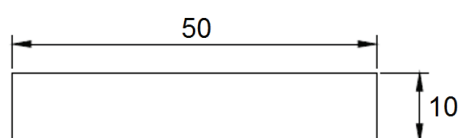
Dimensiones de la platina utilizada para depósitos de soldadura.
